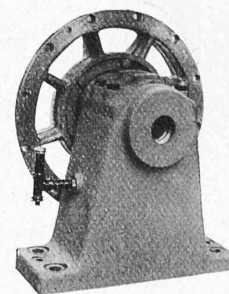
Gemeinsamer Lagerbock beider Rotoren.
